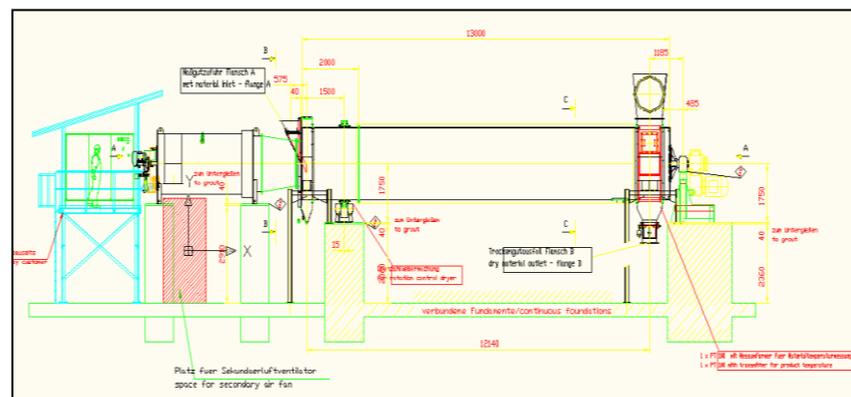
PLANO DE SECADOR – QUEMADOR⁹
